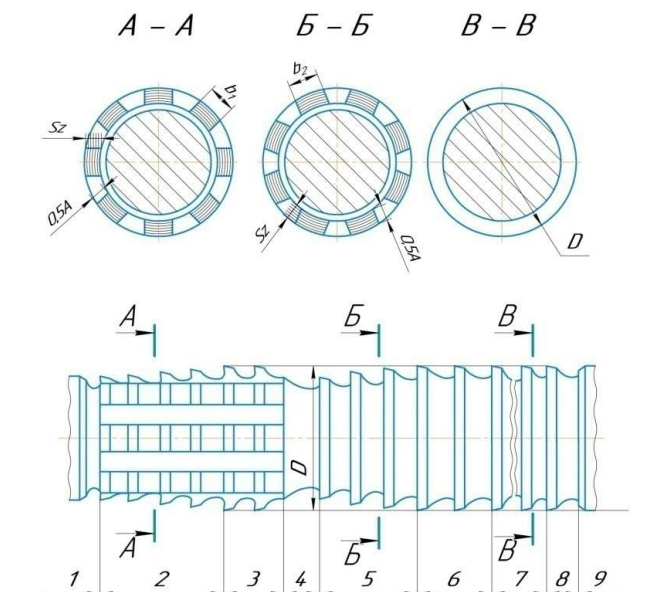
Двухступенчатая прогрессивная протяжка для обработки цилиндрических отверстий
